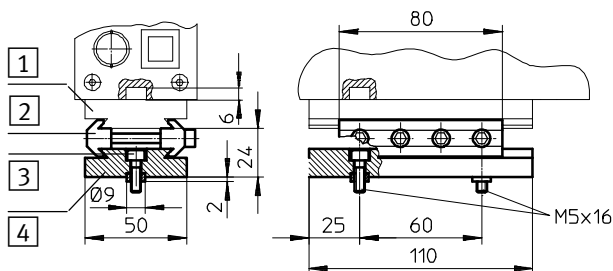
/2: Fissaggio del Checkbox con kit di collegamento HMSV-12
